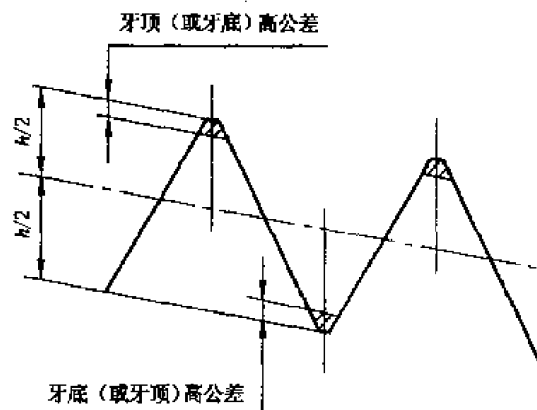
美制一般密封管螺纹的牙顶高和牙底高公差带位置
